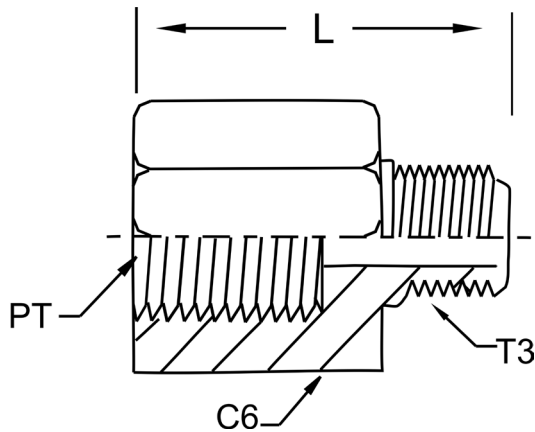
adaptateur de conversion - BSSP à NPTF - dessin dimensionnel
